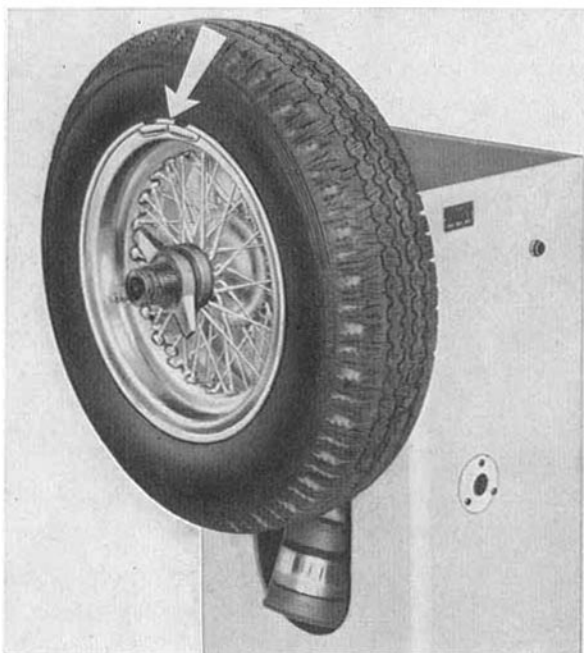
Equilibrage des roues: plaquettes pour l'équilibrage.
